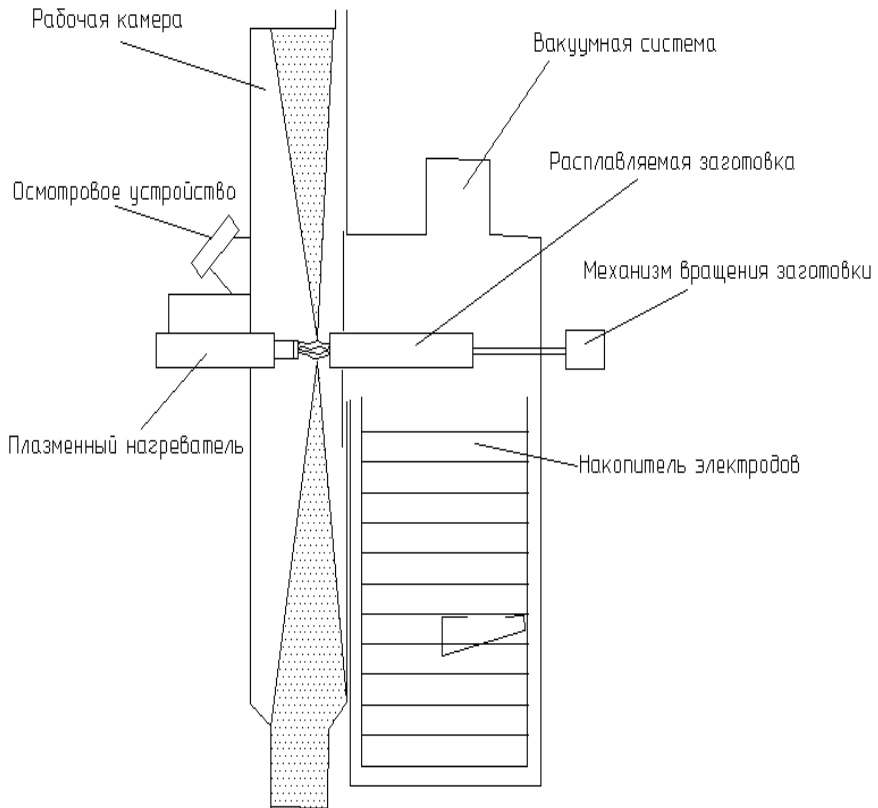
Схема установки по получению металлических порошков ВГУ-2М методом плазменного нагрева и вращением заготовки
